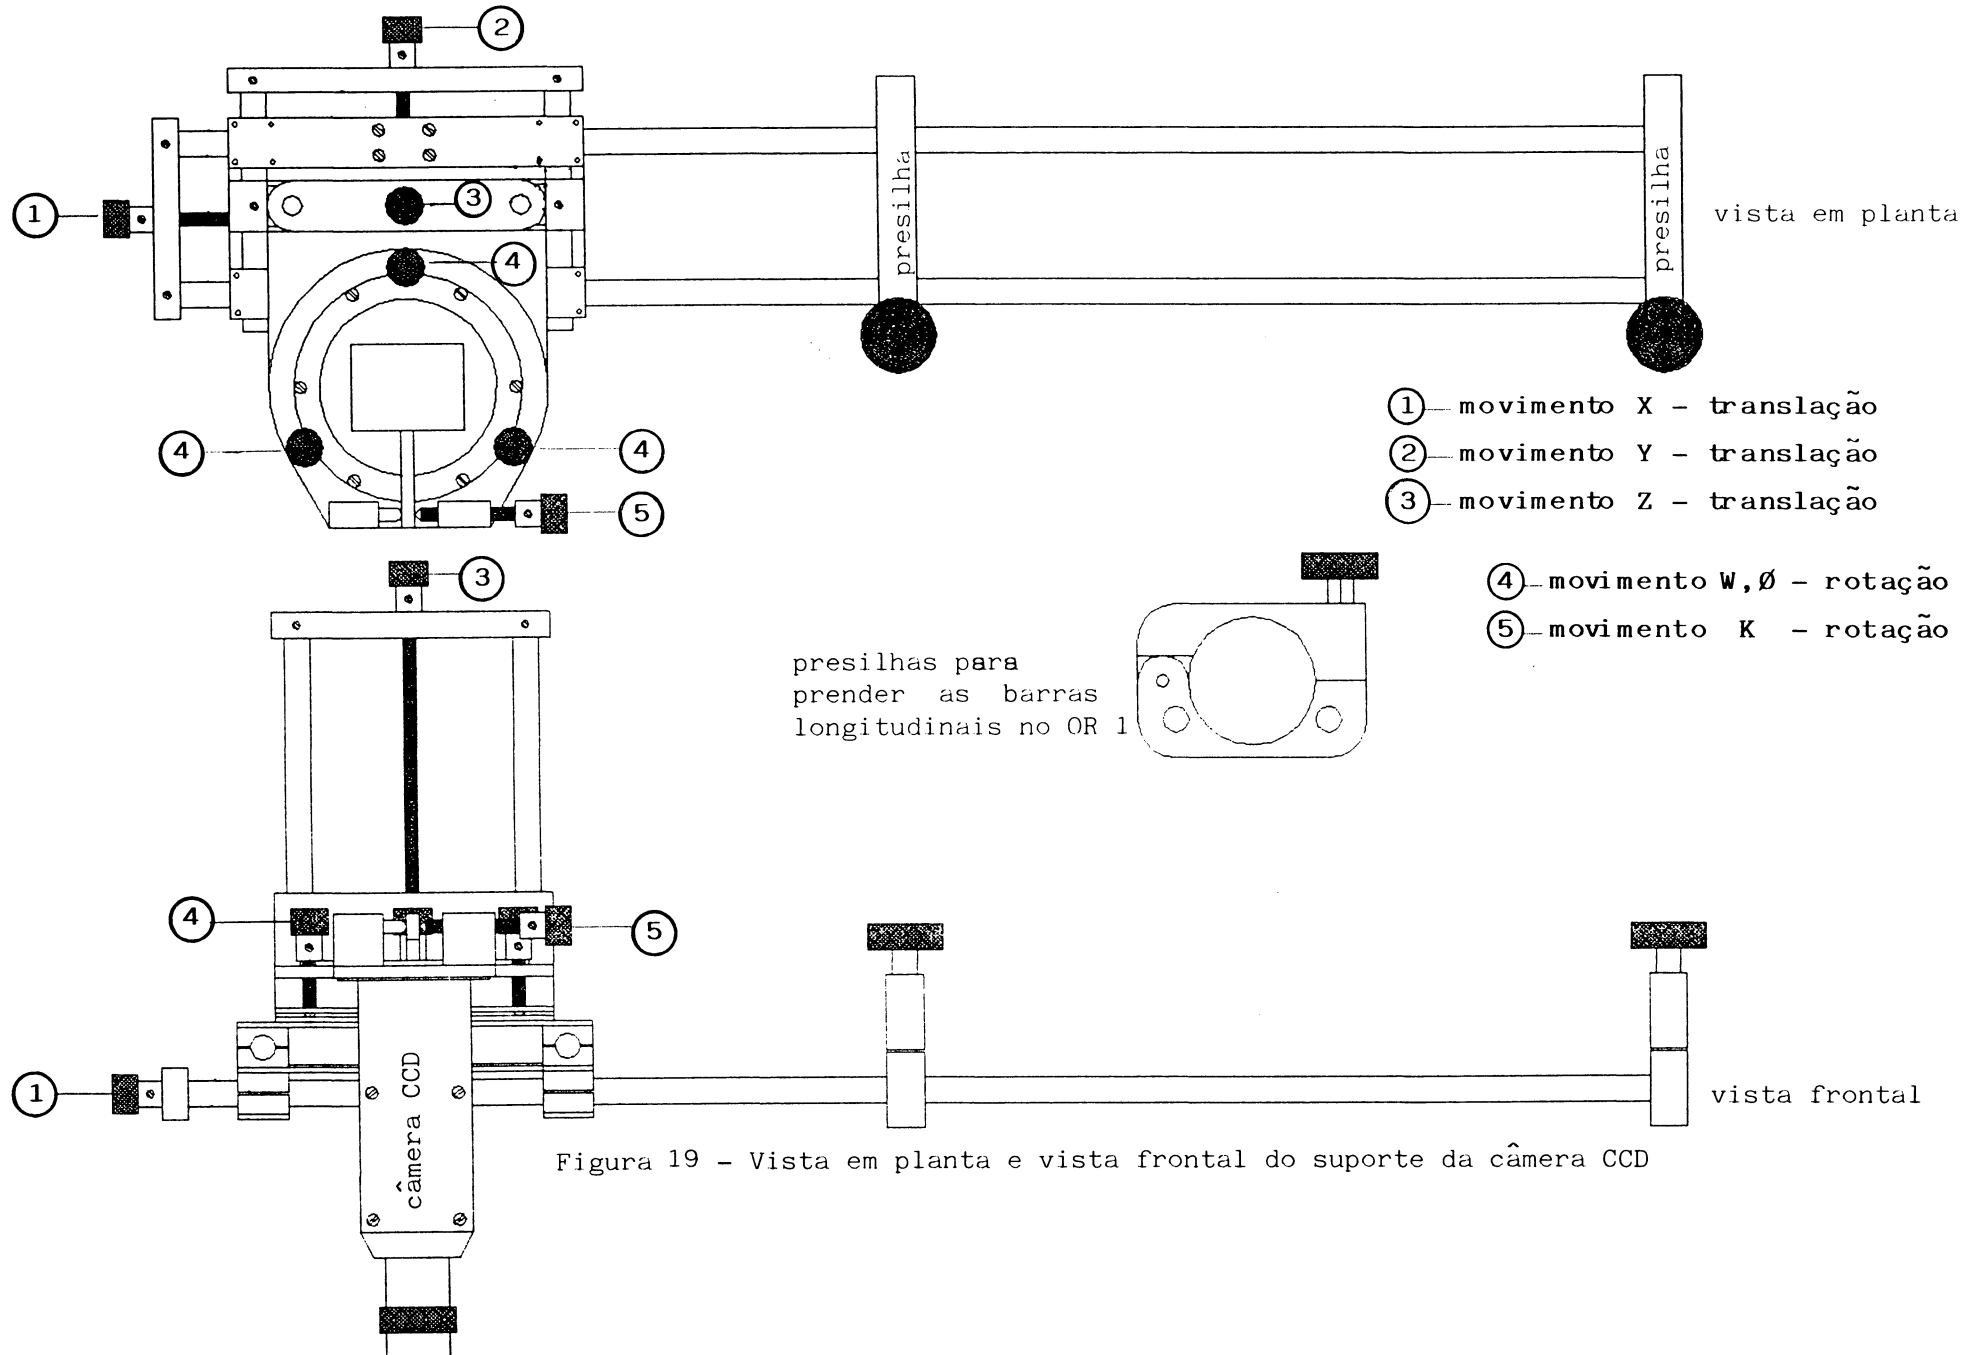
Vista em planta e vista frontal do suporte da câmera CCD
